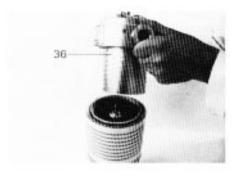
Motor-Lagerschild 36 abnehmen Remove motor part 36 Enlever le flasque du moteur 36
